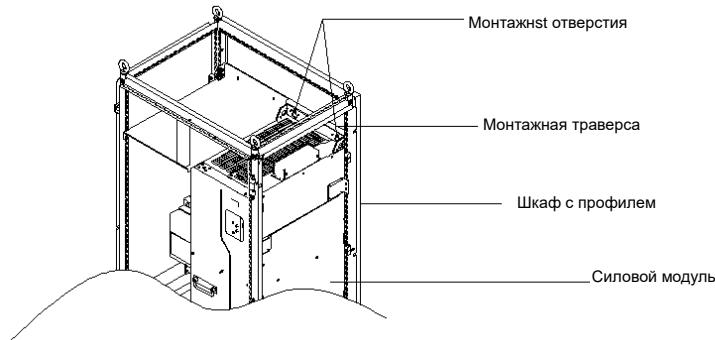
Трехмерный вид крепления GD270-280-4-GD270-500-4 в шкафу
